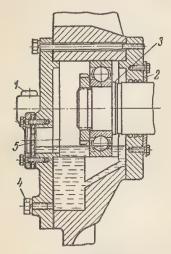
Подшипниковый узел с жидкой смазкой.
